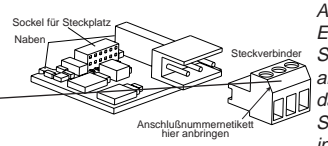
Entfernen Sie den Steckverbinder, und aktualisieren Sie das Etikett, bevor Sie das Modul installieren.
